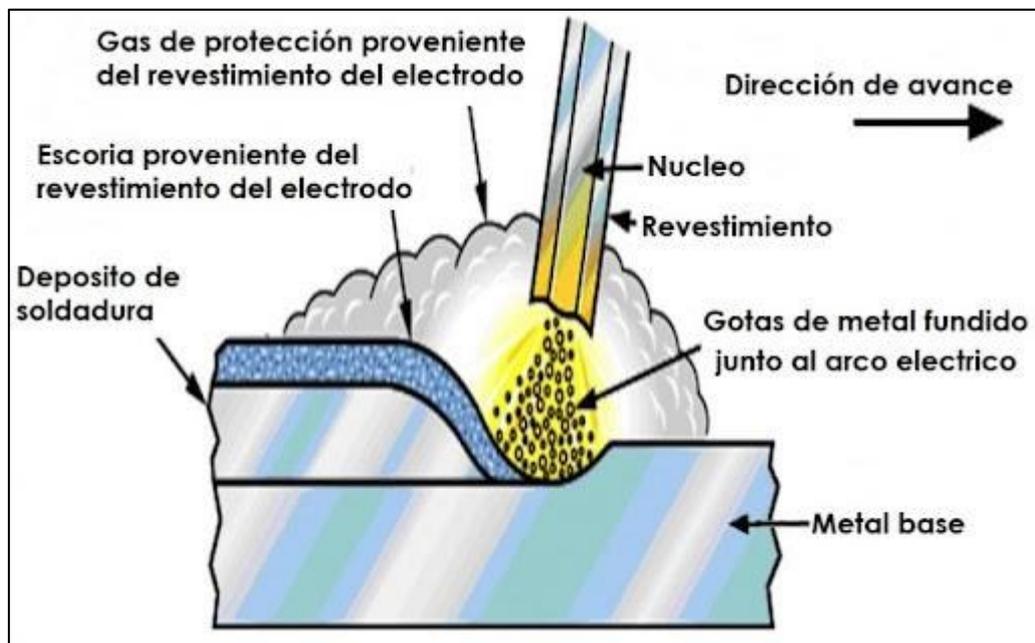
Esquema básico de Proceso de Soldadura SMAW.
